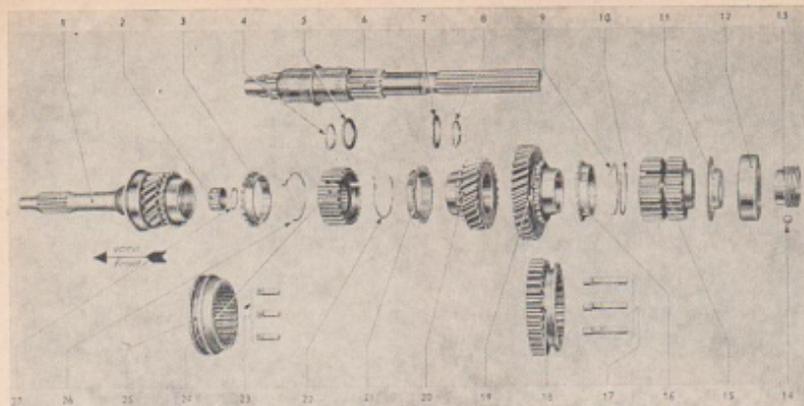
Einzelteile des Hauptwellen-Zahnradblocks mit Hauptantrieb, Montagebild
